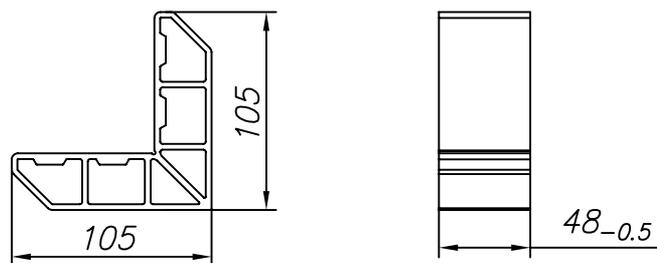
Изготовление соединителя углового FLGU.400.0910
